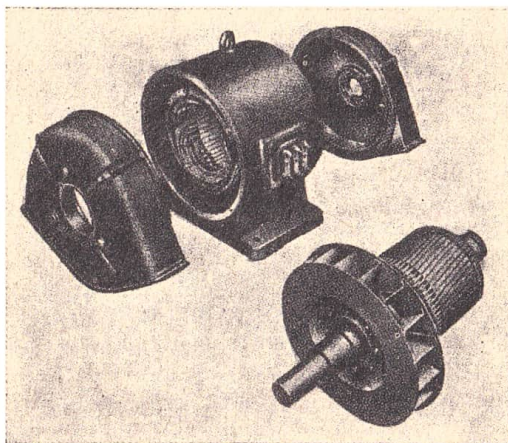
Bestandteile eines Doppelnutmotors, Klemmbrett für Dreieck geschaltet
